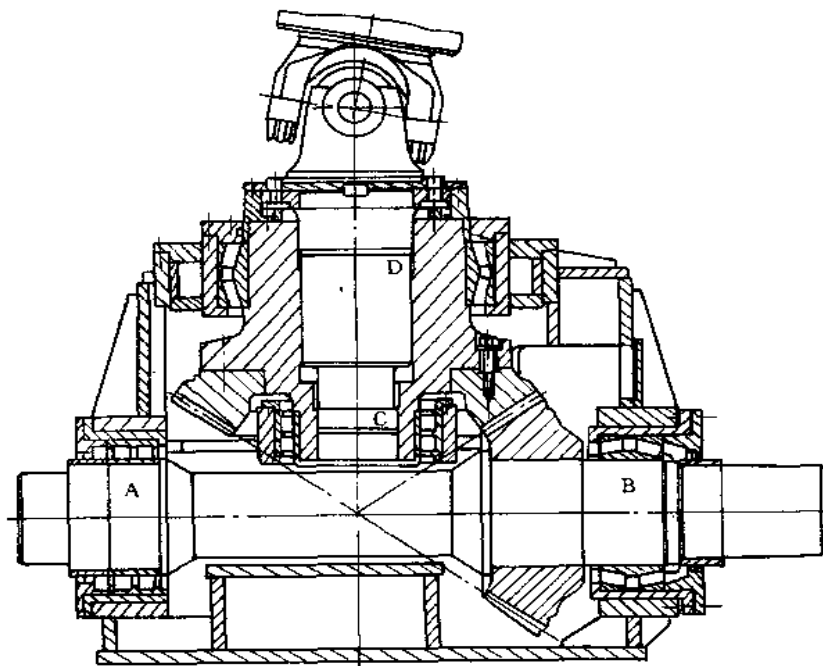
立式轧辊传动机构锥齿轮传动装置支承
